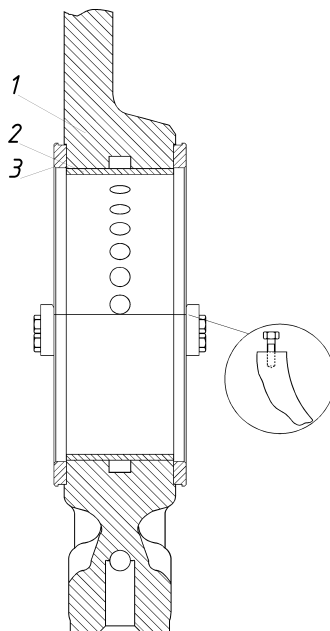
Вкладиші підшипників колінчастого валу. 1 – блок-картер; 2 – вкладиші опорного підшипника; 3 – вкладиші упорного підшипника
